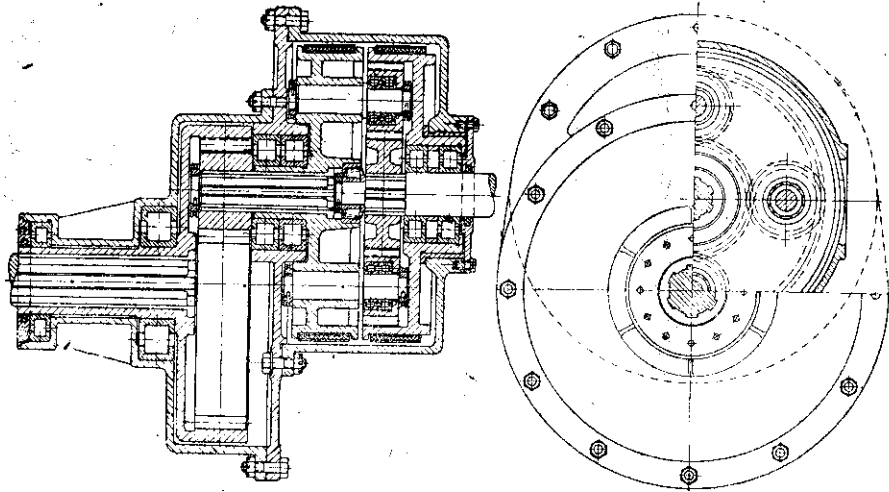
Планетарный одноступенчатый механизм поворота Вильсона.
